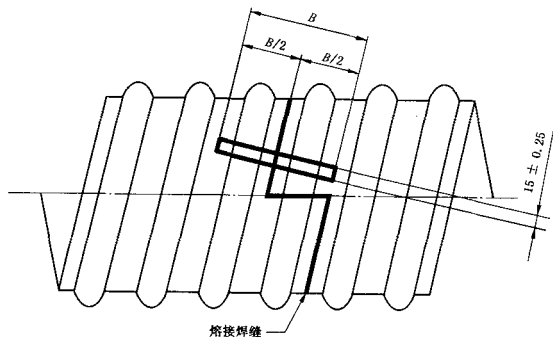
焊缝或熔缝的拉伸强度制备试样的位置和尺寸
